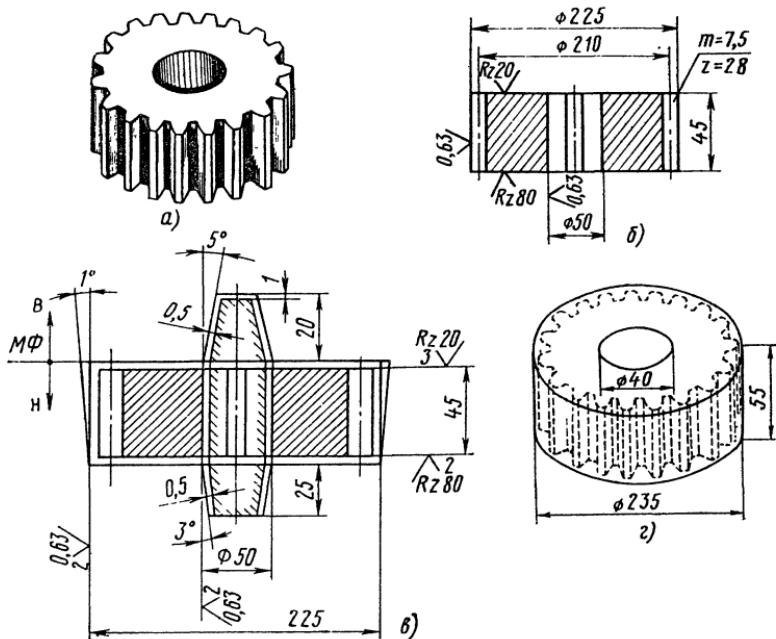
Деталь «Зубчатое колесо» (а), чертеж детали (б), чертеж модельно-литейной технологической разработки (в), чертеж отливки (г)
